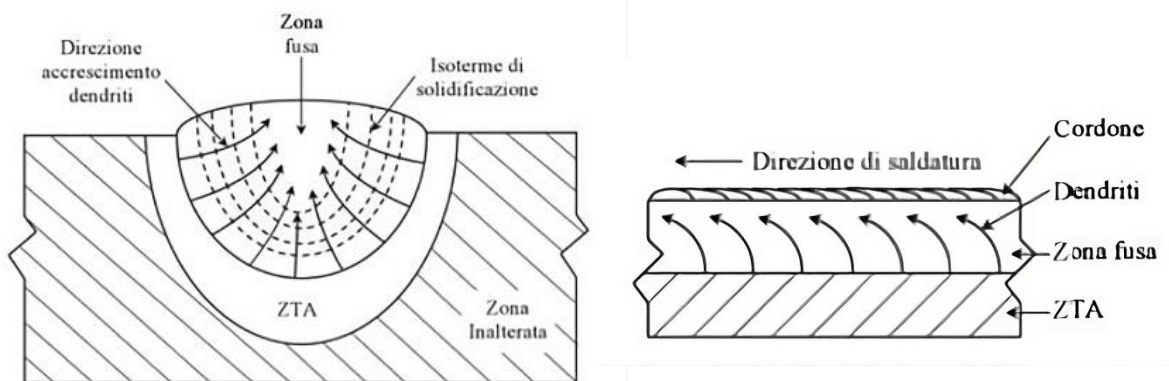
Direzione accrescimento strutture dendritiche rispettivamente in sezione trasversale e parallela alla saldatura. [8]
